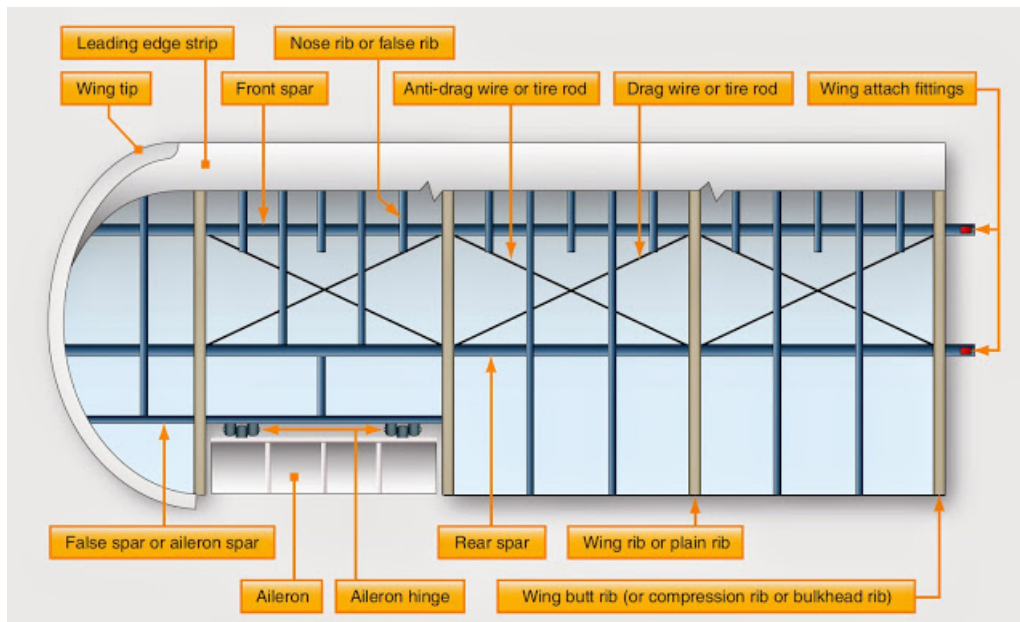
Vista en planta de l'interior de l'estructura d'una ala (aircraftsystemstech)
